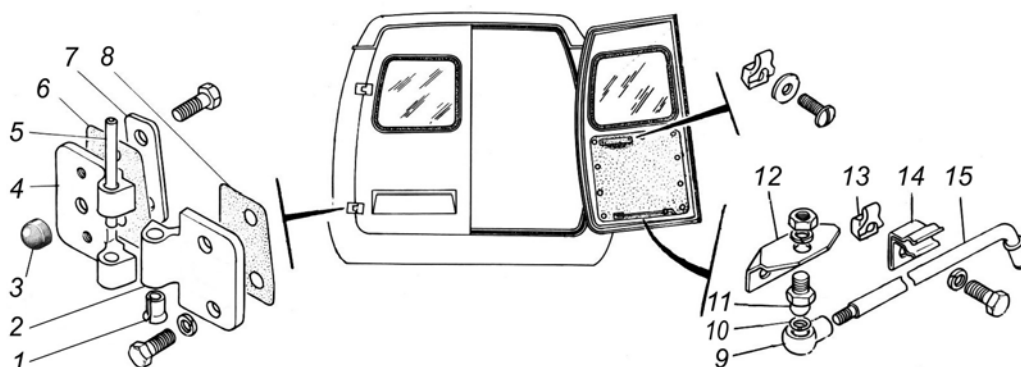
Навеска дверей задка автомобилей со средней крышей: 1 - втулка; 2 - подвижное звено; 3 - буфер; 4 - неподвижное звено; 5 - ось; 6 и 8 - прокладки; 7 - подкладка; 9 - шаровая опора; 10 - стопорное кольцо; 11 - палец; 12 - кронштейн ограничителя; 13 - фланцевая гайка; 14 - зажим; 15 - рычаг ограничителя
